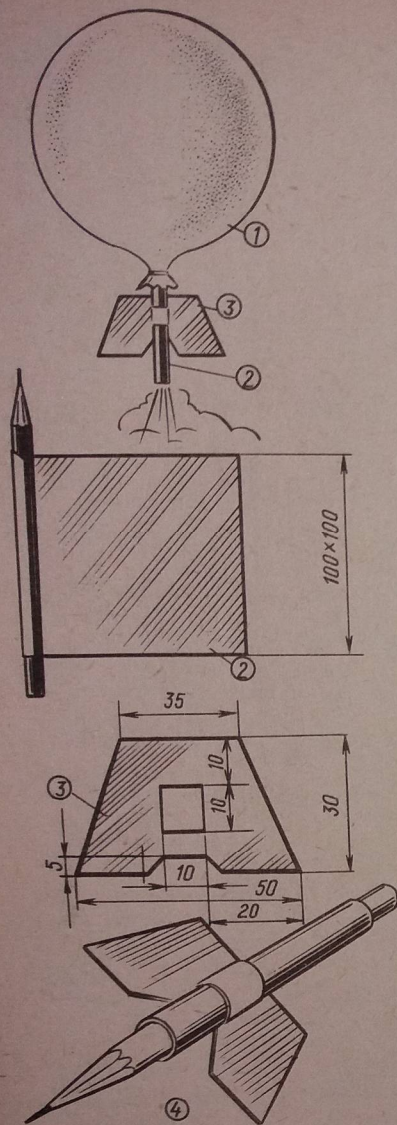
Модель ракеты «Октябренок»: 1 — воздушный шарик (бак с горючим); 2 — изготовление бумажной трубочки (двигателя); 3 — стабилизатор (хвостовое оперение); 4 — сборка двух сборочных единиц (стабилизатора и двигателя)
